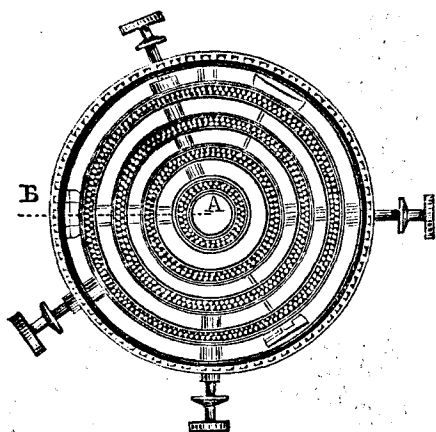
Plan du porte-mèche de la lampe de Fresnel et Arago.
